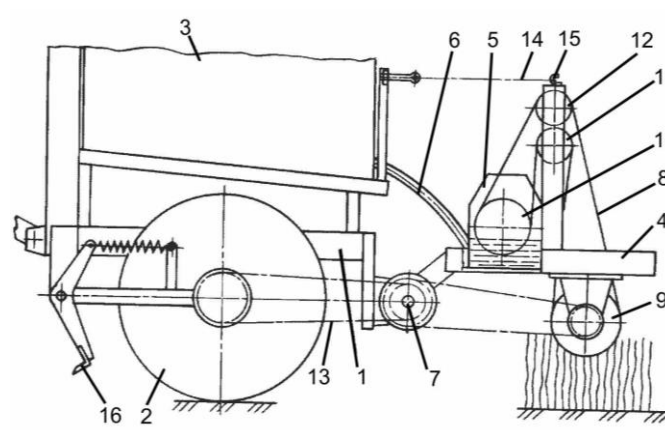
Схема машини для нанесення отрутохімікатів на рослини: 1 – основна рама; 2 – приводне колесо; 3 – резервуар; 4 – допоміжна рама; 5 – робочий резервуар; 6 – трубоповід; 7 – проміжний вал; 8 – полотно; 9 – робочий валик; 10 – валик резервуару; 11; 12 – допоміжні валики; 13 – приводний ланцюг; 14 – натажний ланцюг; 15 – крюк; 16 – скарифікатор
